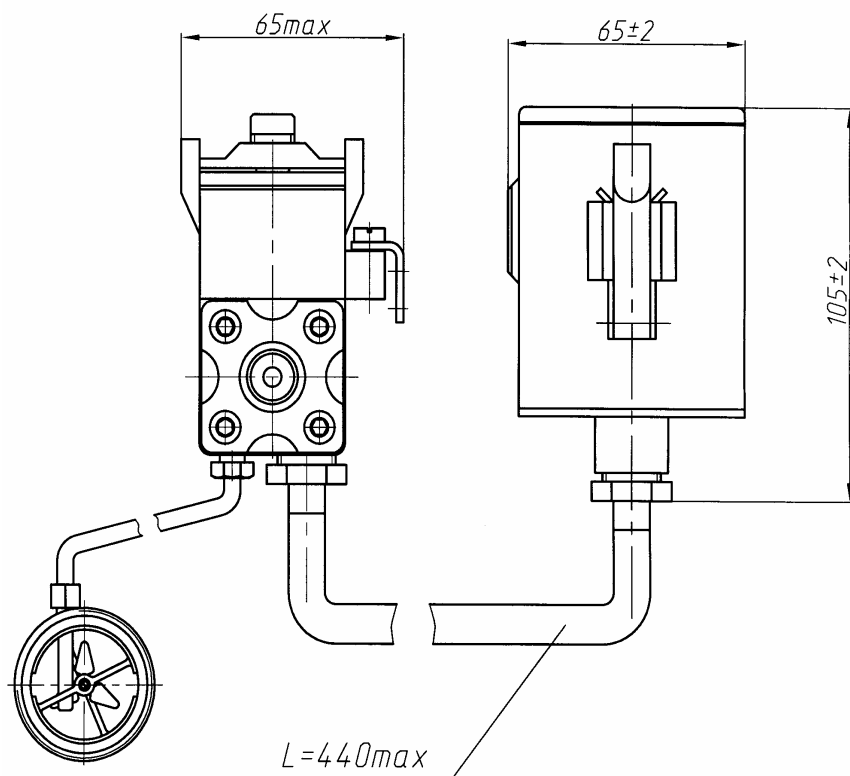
Габаритные и присоединительные размеры (вид 1)
